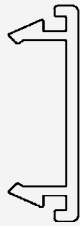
E 32 Befestigungslöcher für die Montage mit Schneidschrauben
